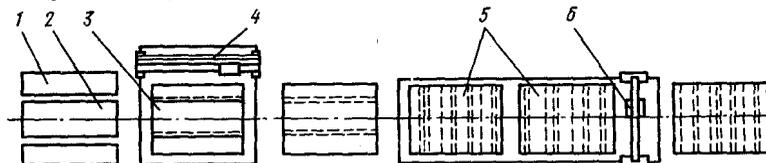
Схема поточной линии сборки и сварки секций крыши электровагона
